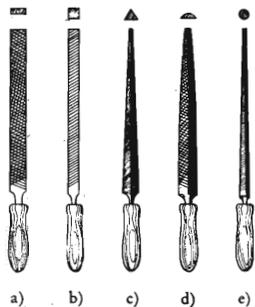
Lime: a) piana, b) quadra, c) triangolare, d) mezza tonda, e) tonda.
